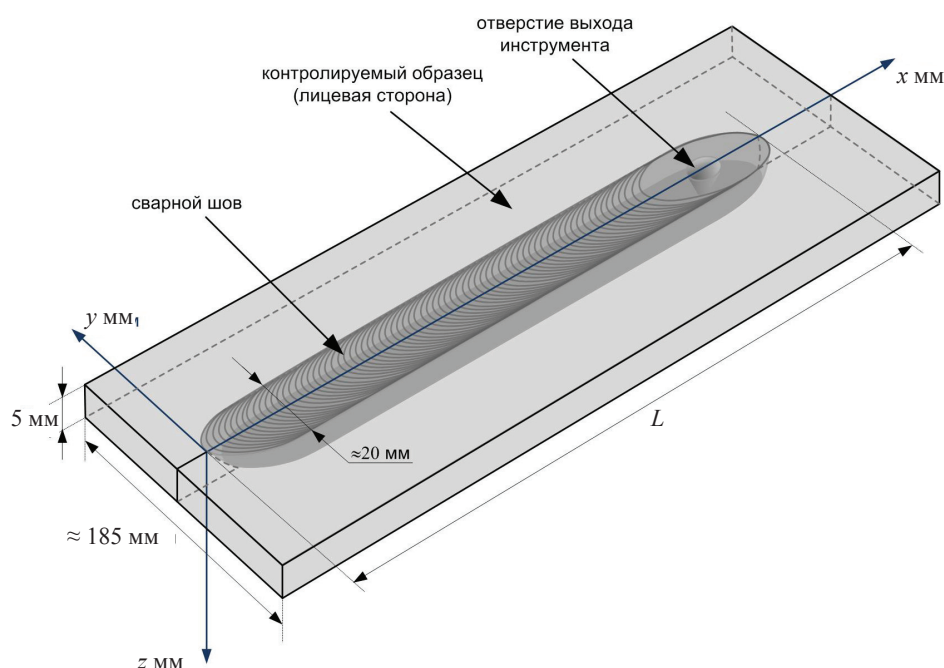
Экспериментальная установка и схема образования сварного соединения
